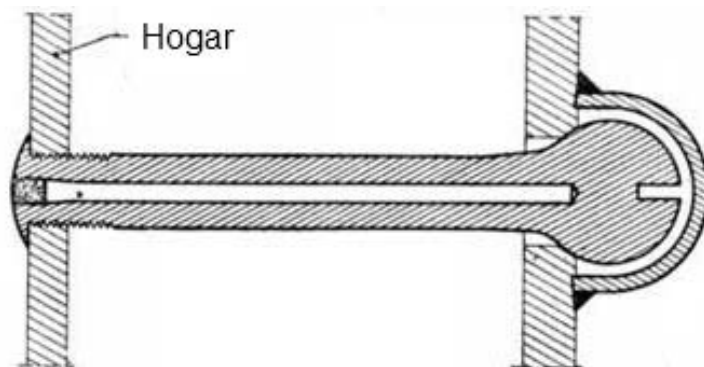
Virotillo con cabeza articulada sin asiento, con sombrero soldado (locomotoras americanas modernas)
